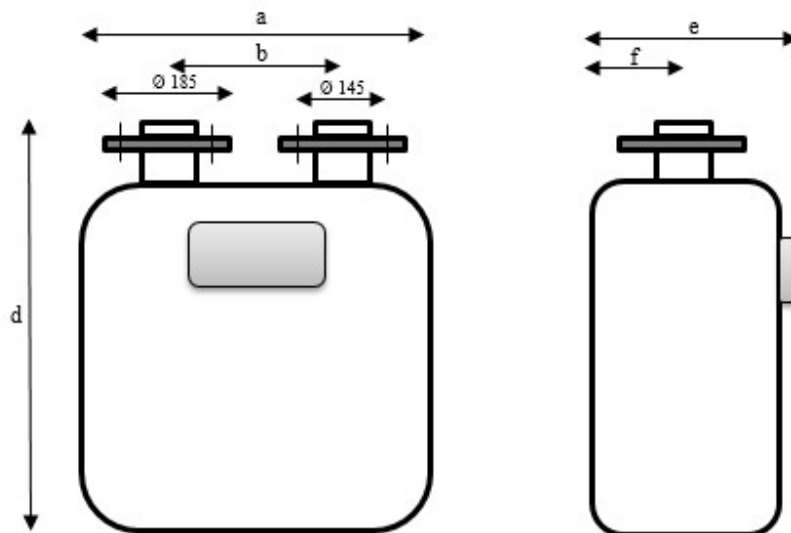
Dimensioni Flange contatori G40 - n. 4 fori (Ø18)
